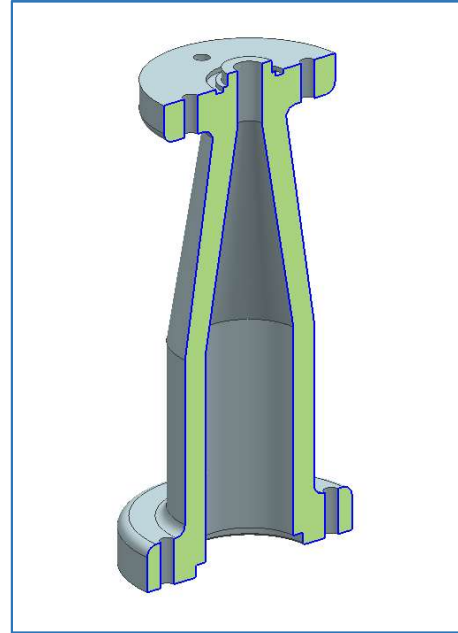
Condotto zona di miscelazione, vista tridimensionale in sezione lungo l'asse
